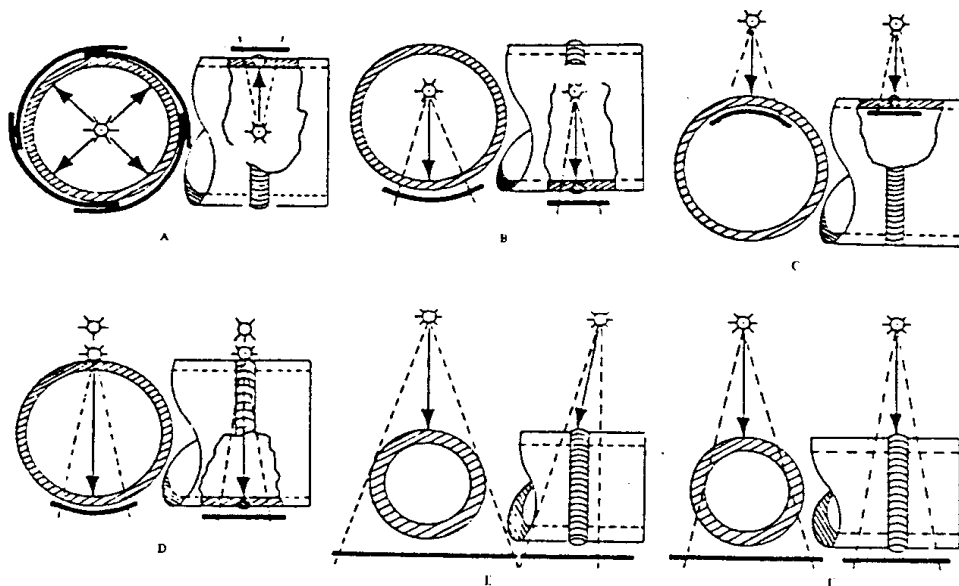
Radiografiado de soldaduras circulares a tope.
